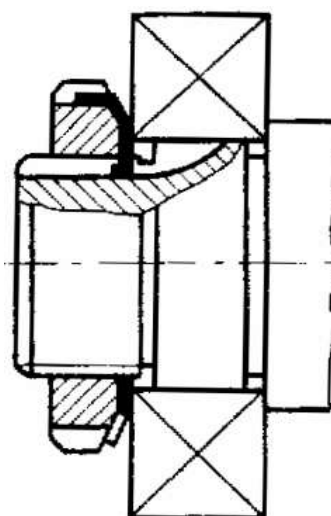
Способы закрепления внутреннего кольца подшипника на валу:
